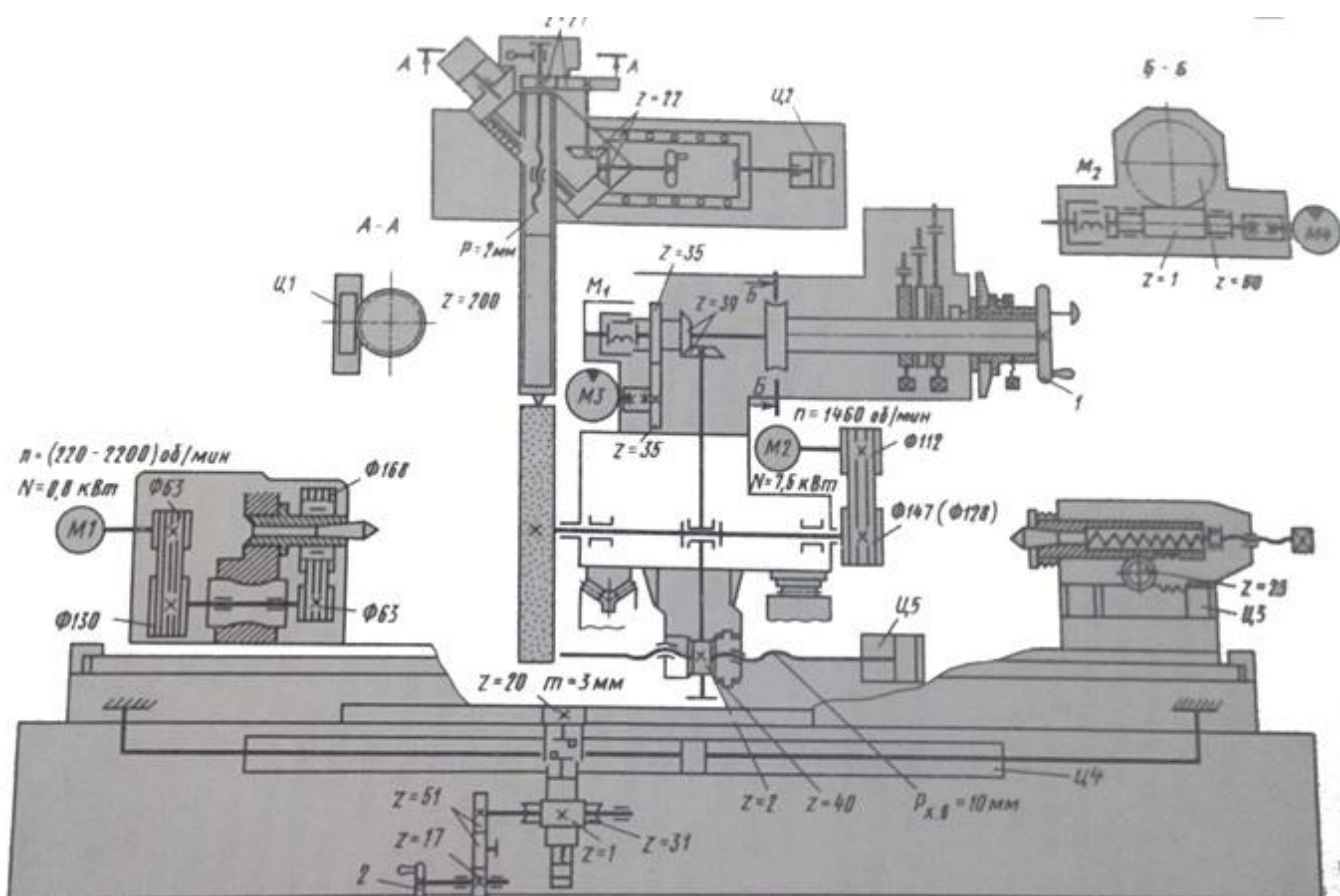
Кинематическая схема круглошлифовального станка модели 3М151
